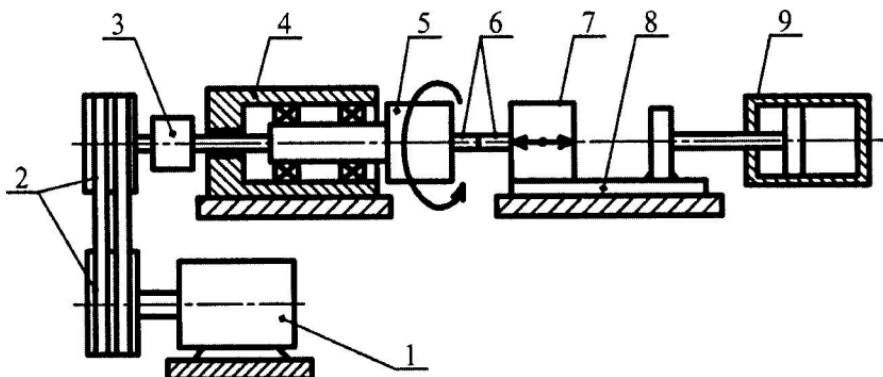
Принципова конструктивно-кінематична схема машини для зварювання тертям
